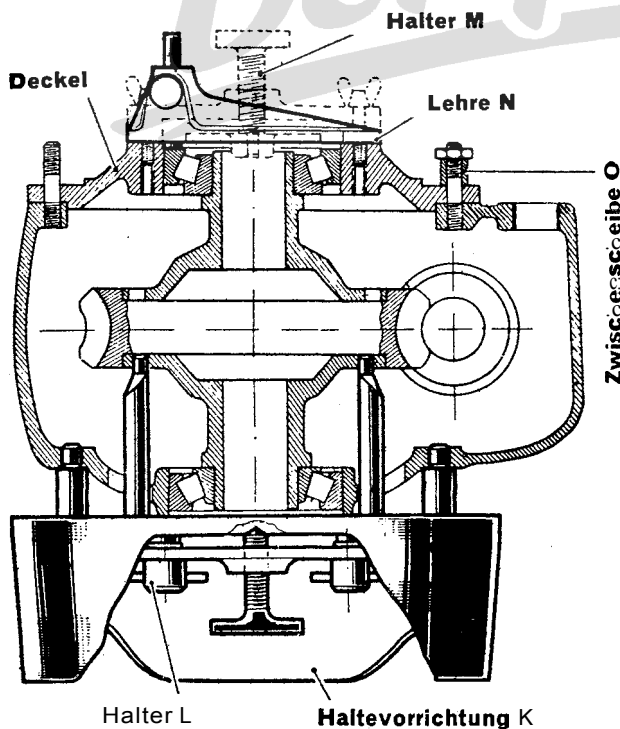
Peugeot 403, Messung des zusammengebauten Achsantriebes.
